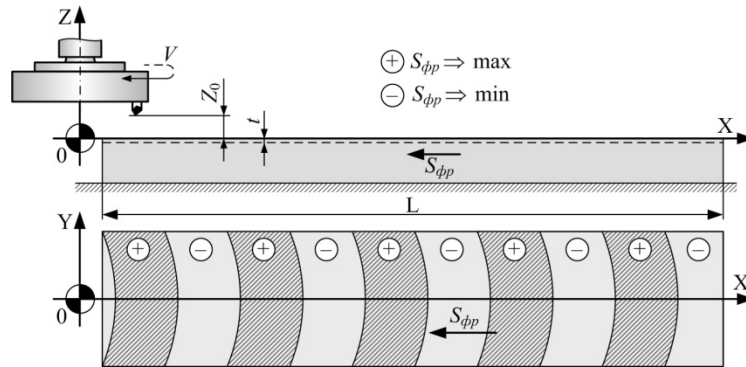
Схема торцевого фрезерования композитом 10 плоской поверхности заготовки с дискретным изменением величины подачи $S_{фр}$ на станке с ЧПУ
